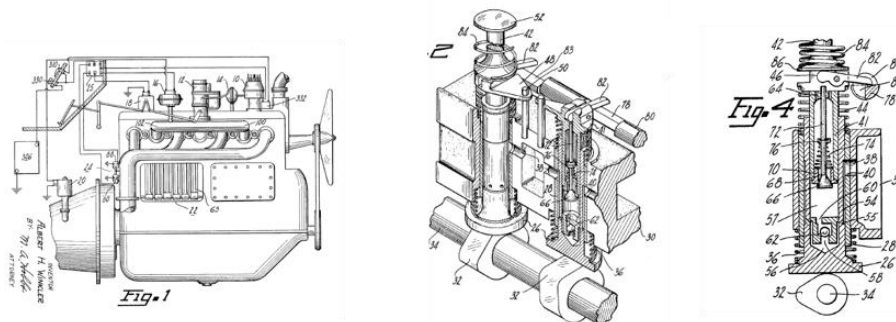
Zylinderabschaltung mittels hydraulischem Mechanismus 1956 [113]
